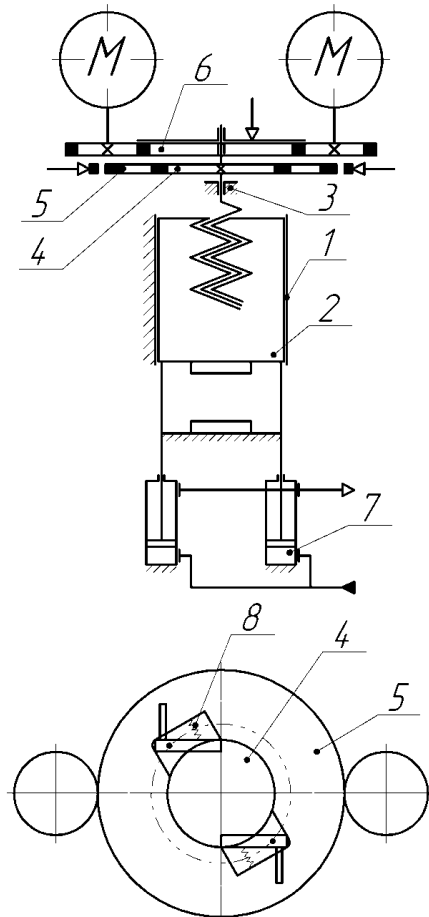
Кінематична схема гвинтового преса (1 – станина; 2 – повзун; 3 – гвинтовий шпindelь; 4 – внутрішній маховик; 5 – зовнішній маховик; 6 – ведуча частина (маховик); 7 – зворотній привід; 8 – пружини)
